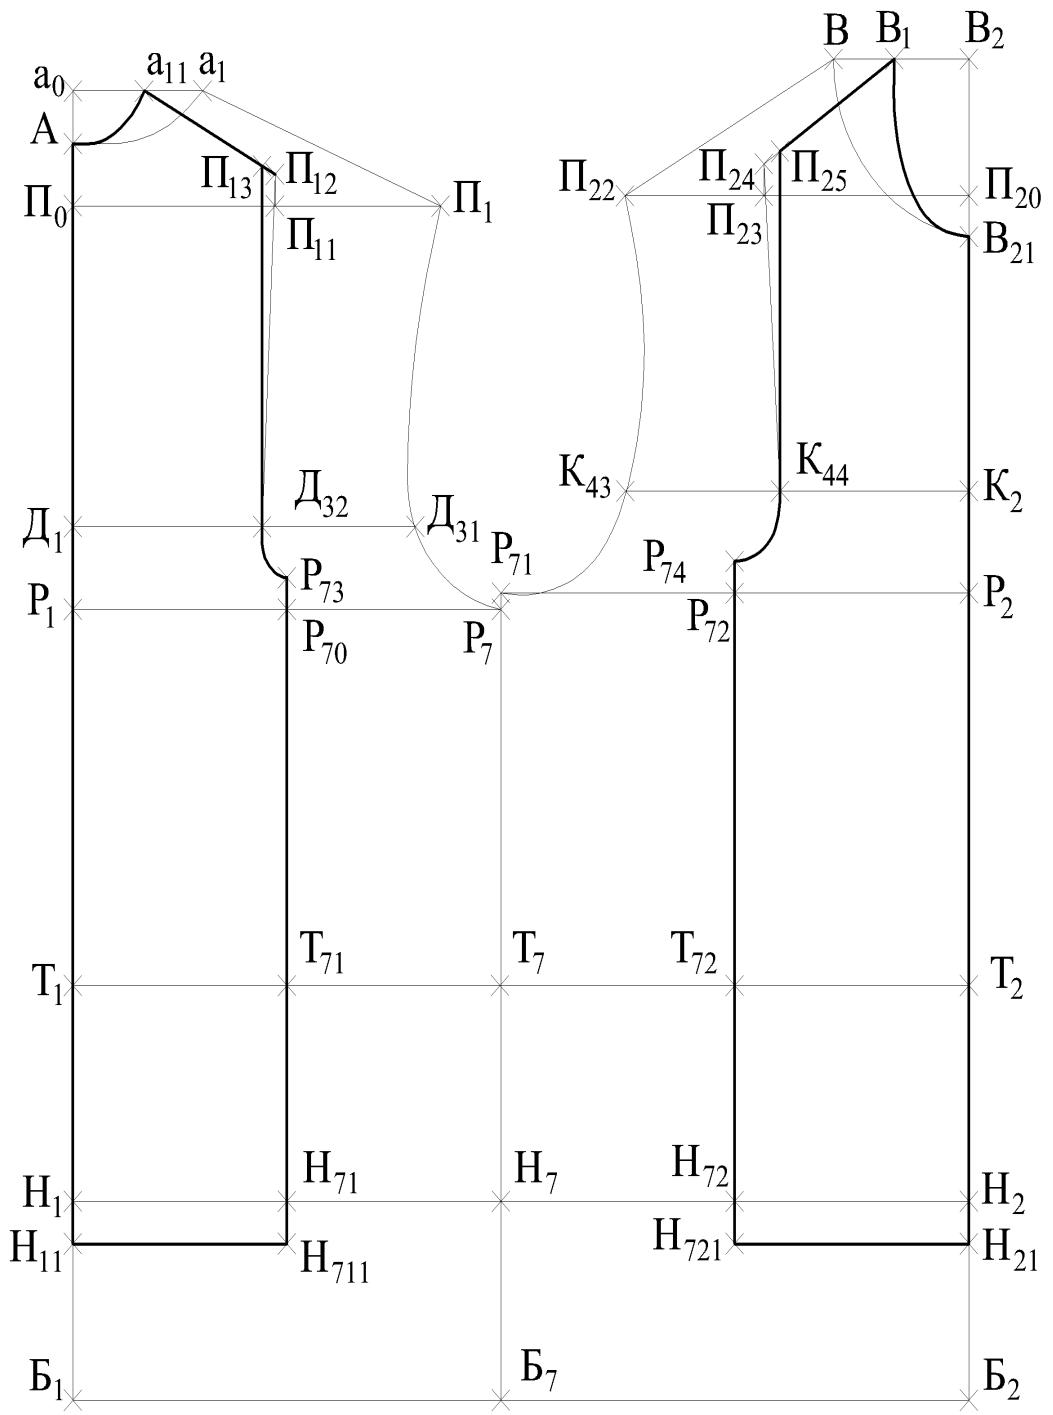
Чертеж конструкции спинки и переда джемпера полурегулярного с заужением
